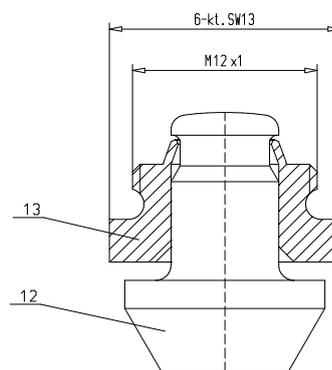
Kegel-Ø 8mm PAW 6610.8051
